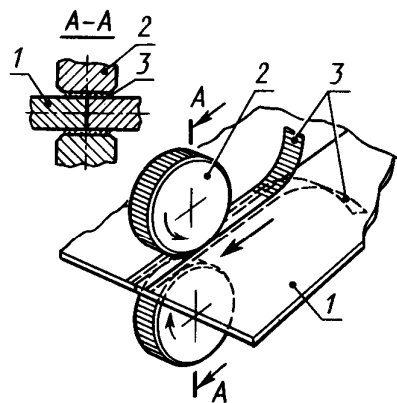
Принципиальная схема шовной стыковой сварки с применением стальных лент
